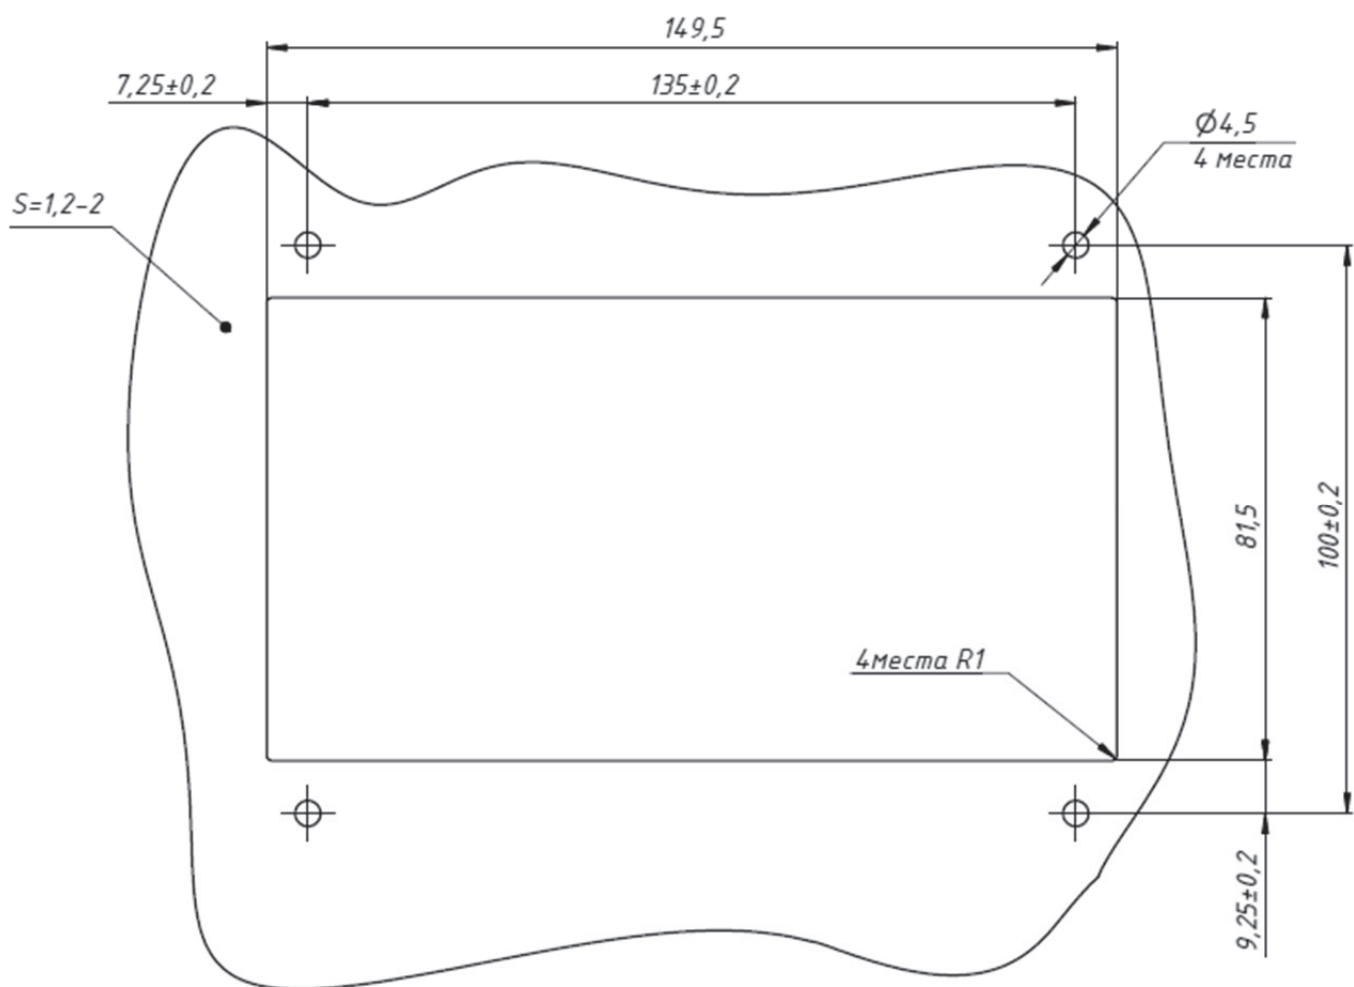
Чертеж места установки установки ПРОЭЛ-МИНИ-02
